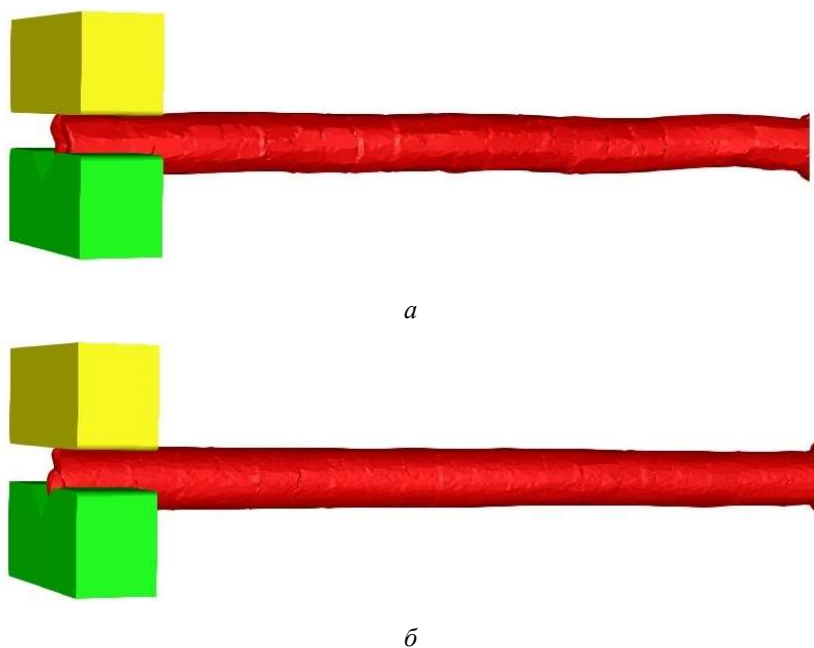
Форма заготовки в процессе ковки: а – при ковке по схеме 1; б – при ковке по схеме 2
